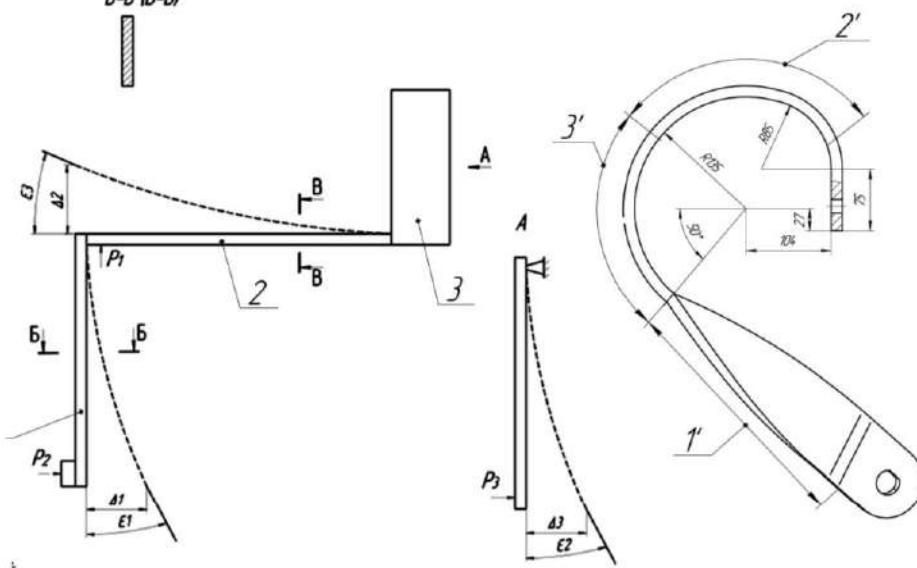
Розрахункова схема до обґрунтування конструкції стояка
